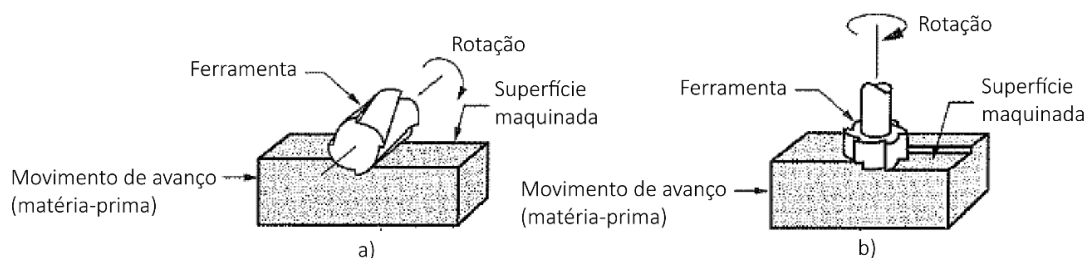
Métodos de fresagem: a) periférica ou cilíndrica; b) de topo ou frontal (adaptado de [2]).
